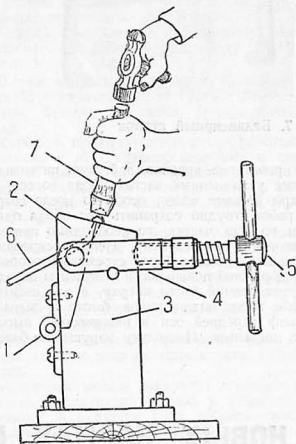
Приспособление для штамповки головок спиц и загиба их
